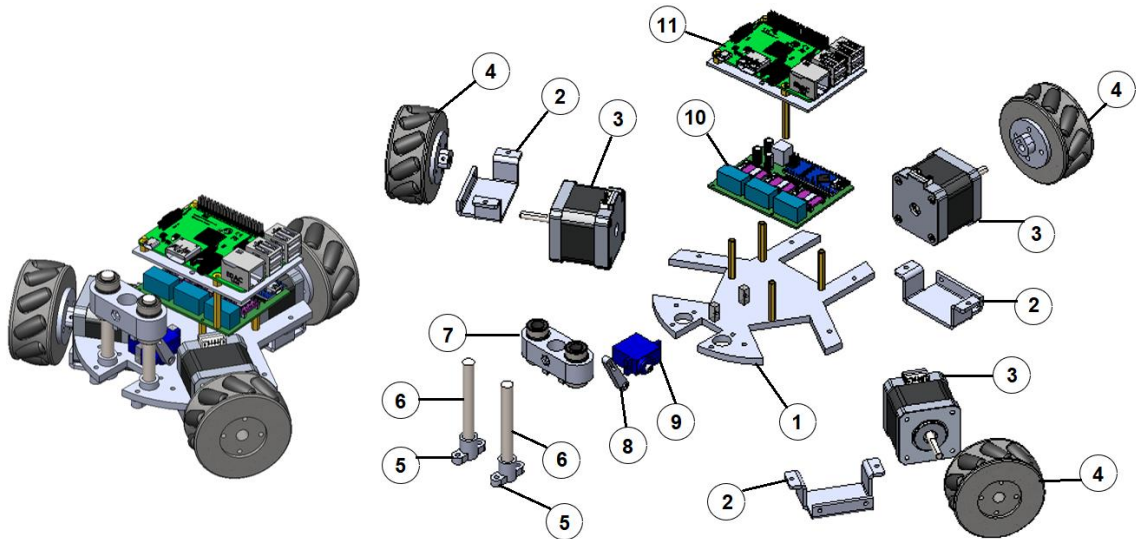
Vista isométrica y explosionada respectivamente del robot final
